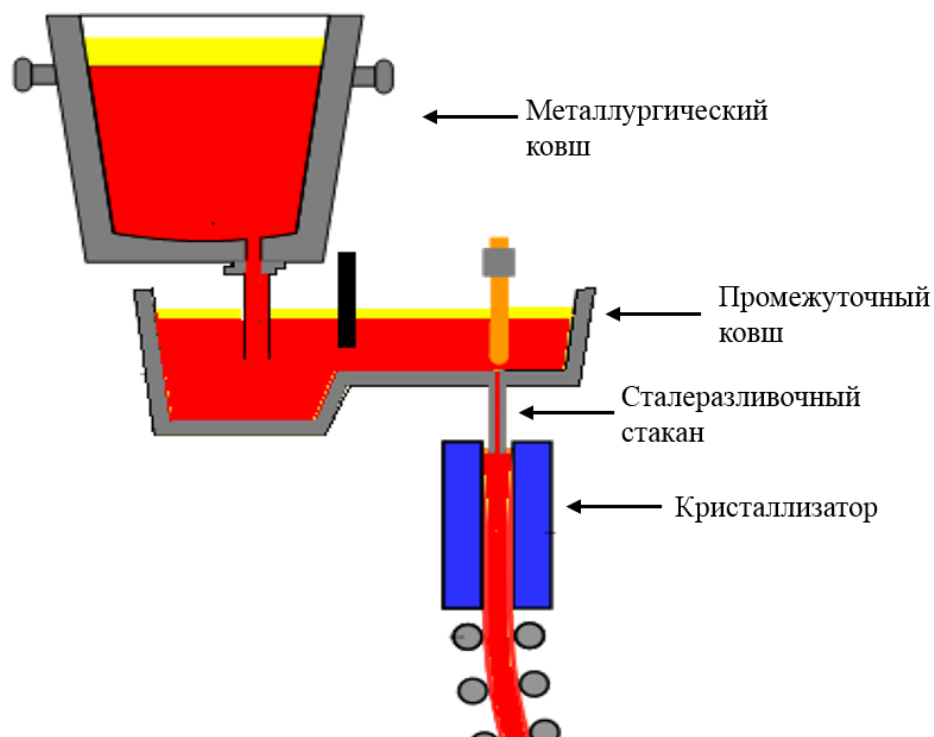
Сталеразливочный стакан на схеме машины непрерывного литья заготовок.
